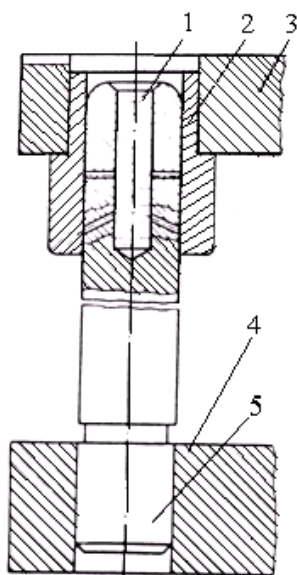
Конструкция направляющих элементов штампа со свободной подачей смазки
